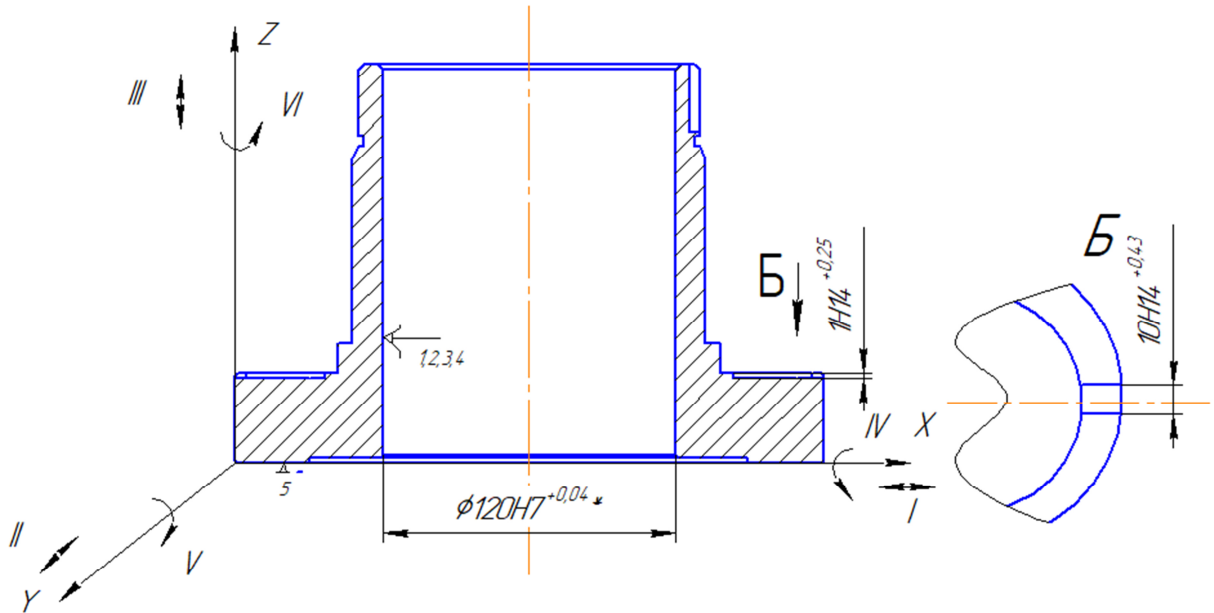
Схема базування заготовки (Позиція II).
